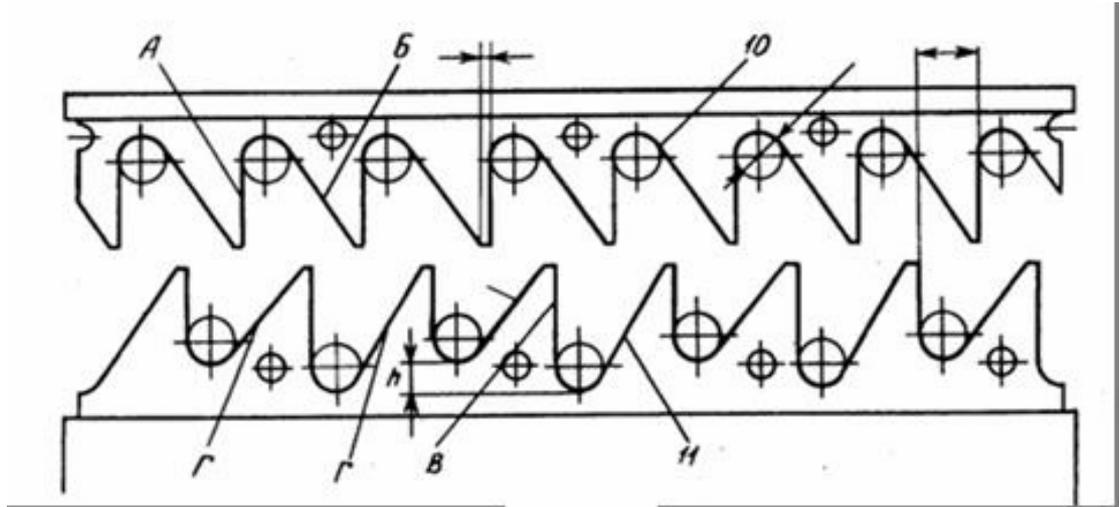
Развертка фигурного паза толкателя (А.С. SU1344567)
